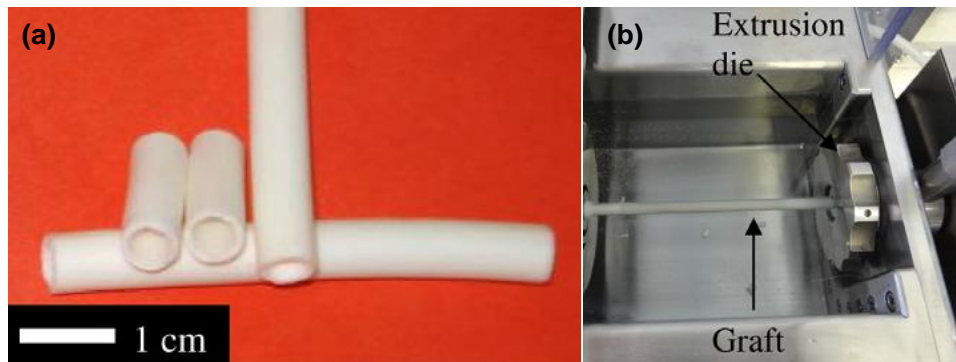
(a) Implantes de pequeño diámetro producidos por extrusión [57]; (b) máquina de extrusión diseñada para producir implantes de pequeño diámetro [57].
